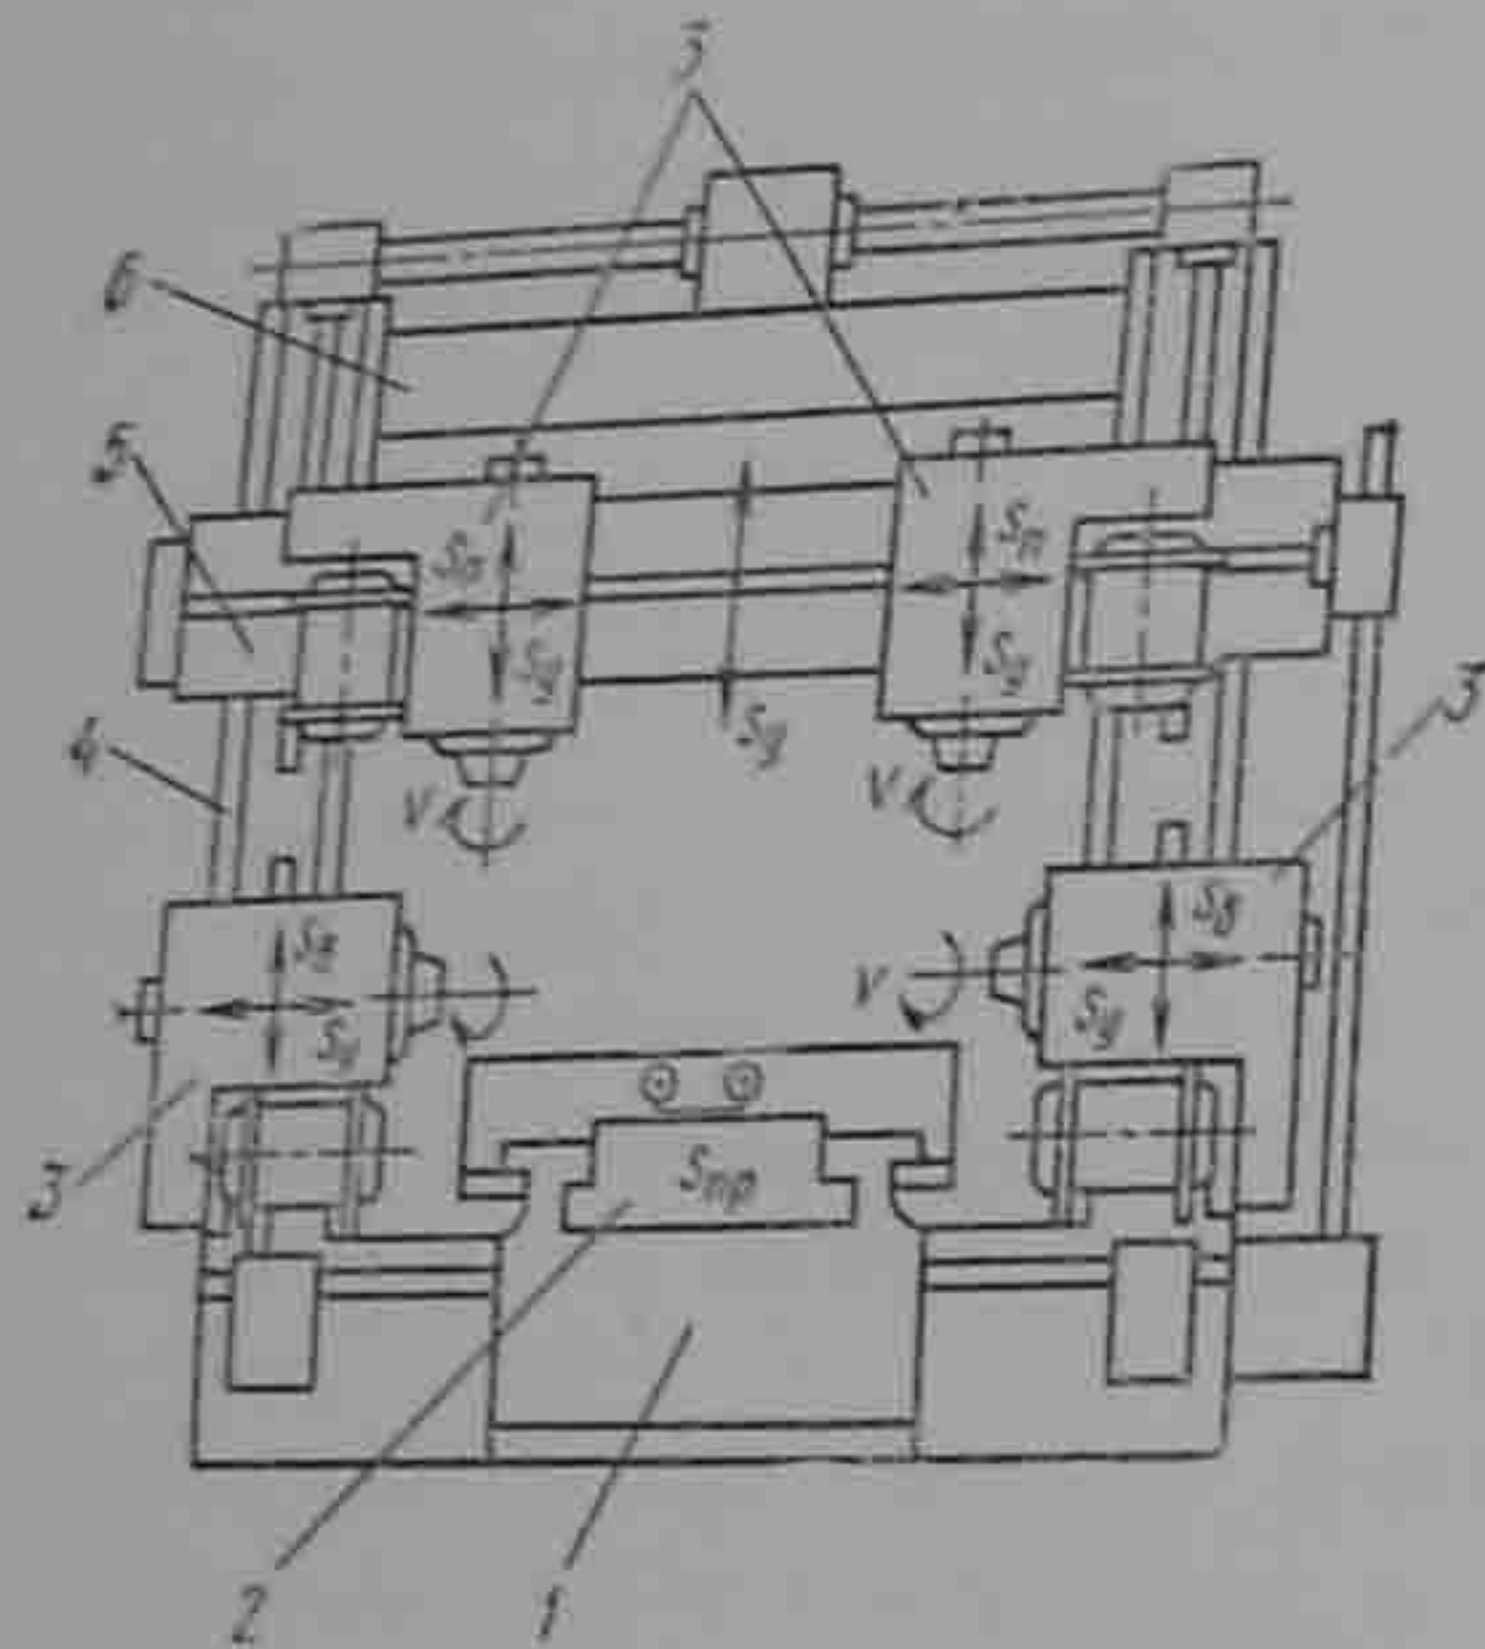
Общий вид продольно-фрезерного двухстоечного станка
